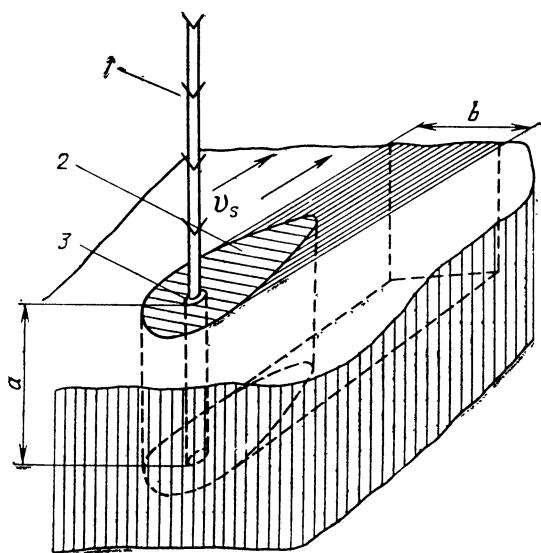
Схема при сварке с глубоким проплавлением лучом мощных лазеров:
